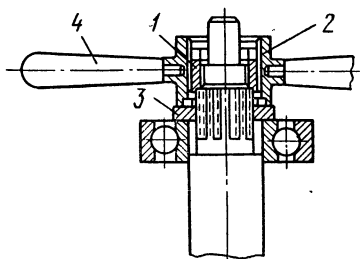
Гайечное приспособление для напрессовки подшипников:
